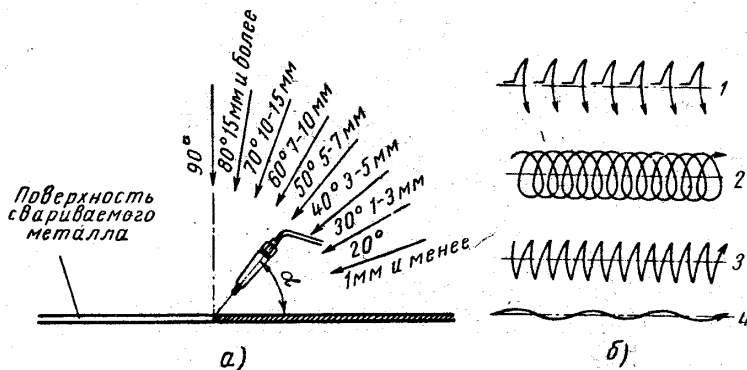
Углы наклона (а) и способы перемещения (б) мундштука при газовой сварке
